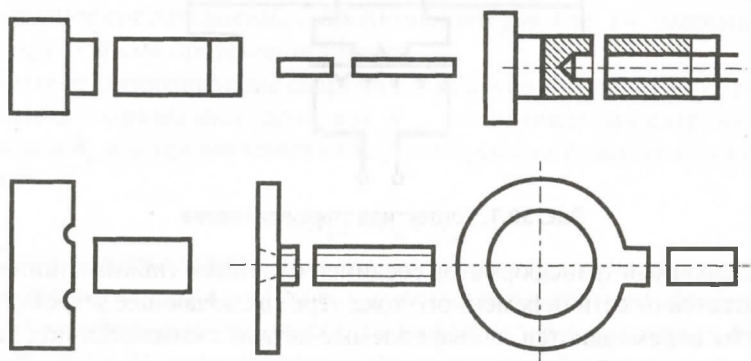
Типы сварных соединений стыковой сварки сопротивлением
